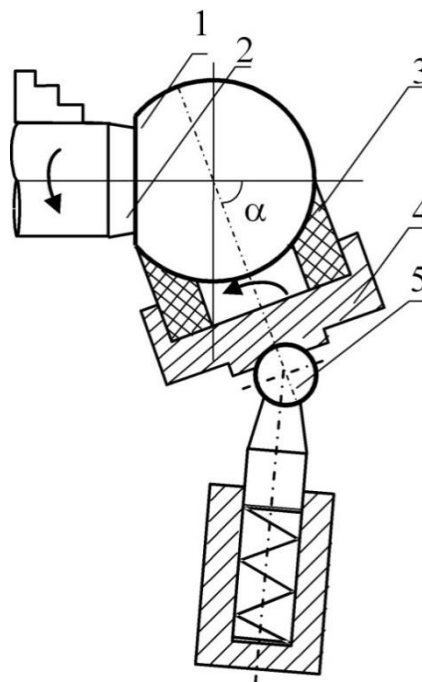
Схема абразивной обработки заготовки свободной притиркой
